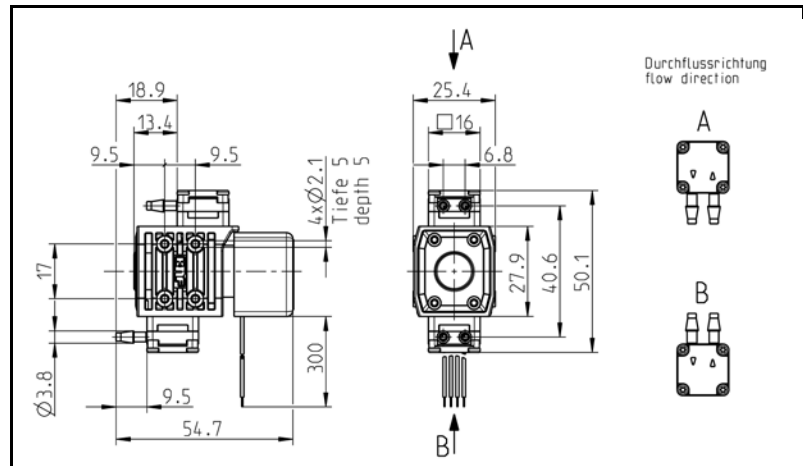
Befestigungsmasse NFB 5 DCB-4
